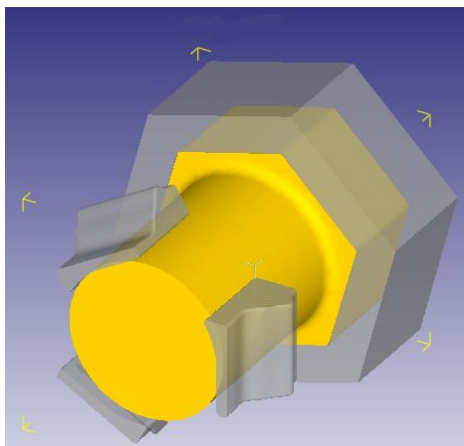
Твердотельная модель устройства для моделирования процесса профилирования заднего конца заготовки
